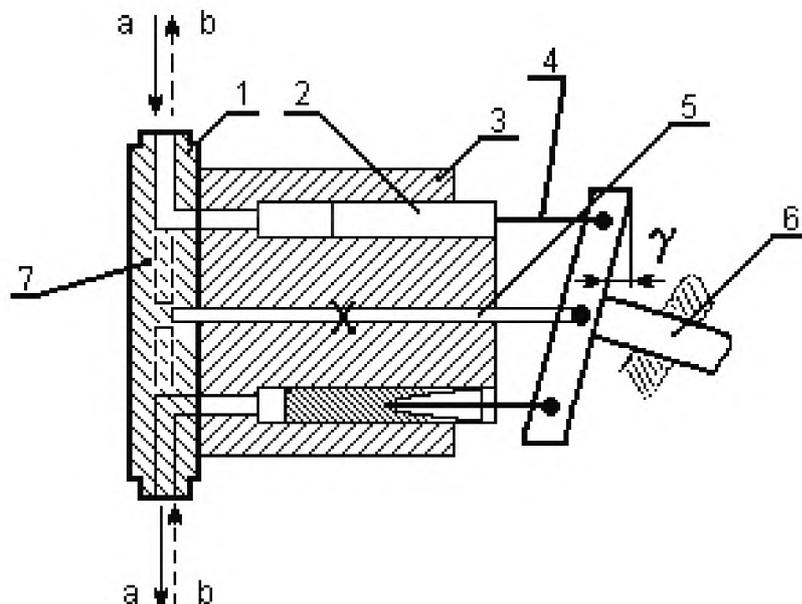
Аксиально-поршневой насос: 1 - распределительный диск; 2 - поршень; 3 - барабан; 4 - шток; 5 - ось; 6 - вал, 7 - корпус распределителя
